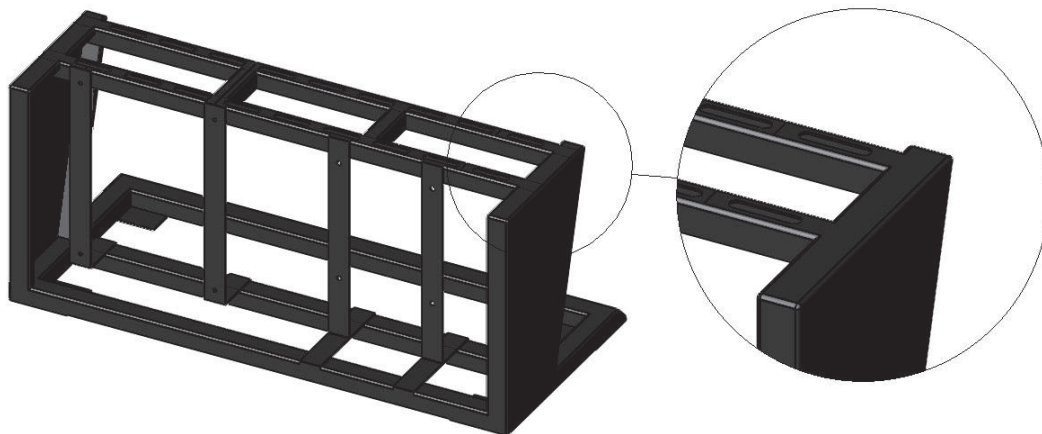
Detalle de soldadura en estructura soporte.
